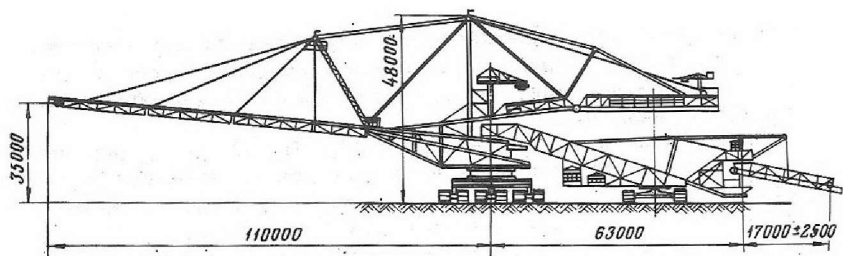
Конструктивная схема отвалообразователя ARs-B.8800.110
